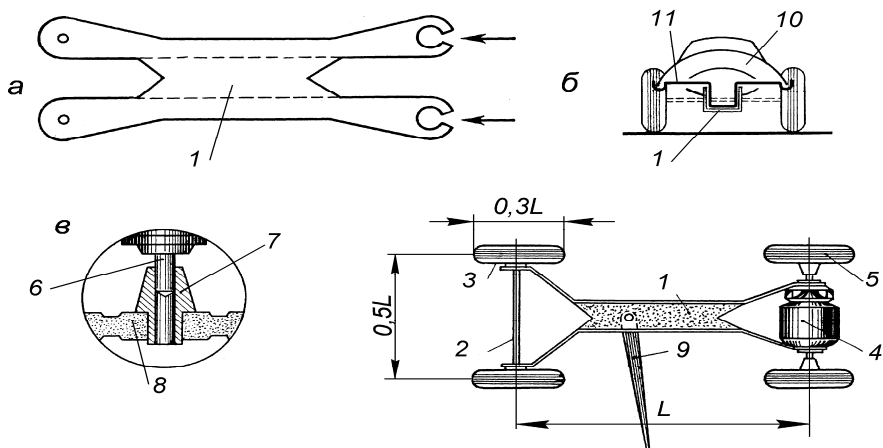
Схема розташування деталей і складання кордової швидкісної моделі автомобіля: а - характер розгортки несучого шасі; б - елементи конструкції кріплення кузова; в - варіант кріплення задньої провідної осі до колеса; г - конструкція автомобіля при вигляді зверху
